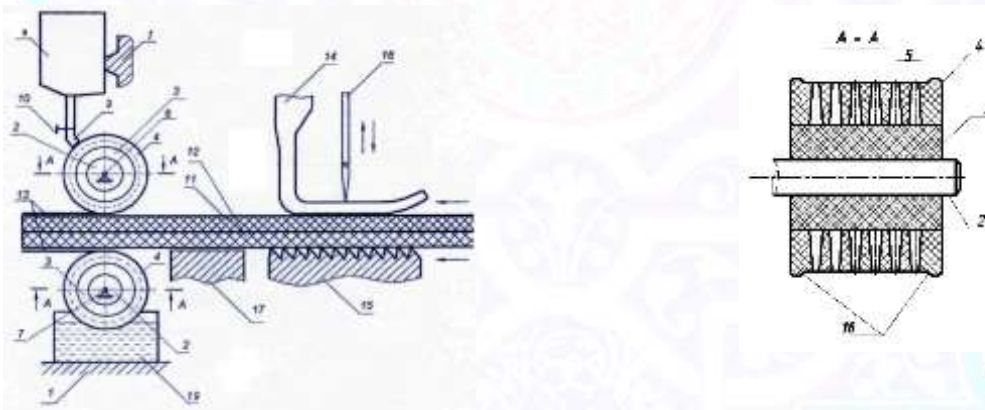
Устройства для нанесения полимерной композиции на стачиваемые детали края
